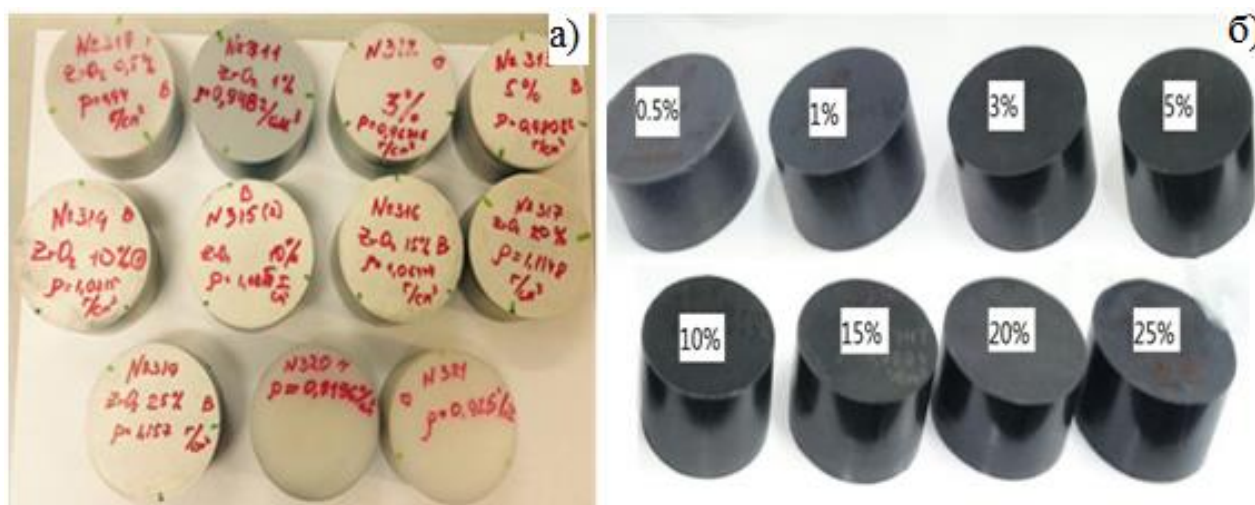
а) Заготовки с ZrO_2 ; б) Заготовки с УНТ
